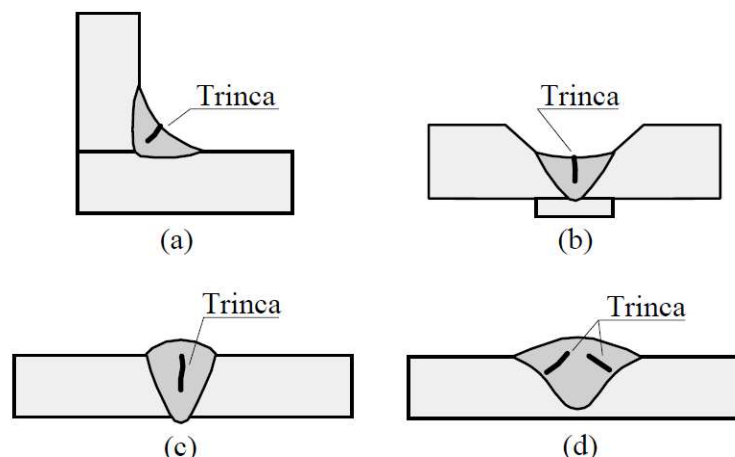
Formação de Trinças de Solidificação em (a) cordões côncavos em soldas de filete, (b) cordões côncavos em passe de raiz, (c) soldas de topo com elevada razão penetração - largura e (d) em cordões em forma de sino.
